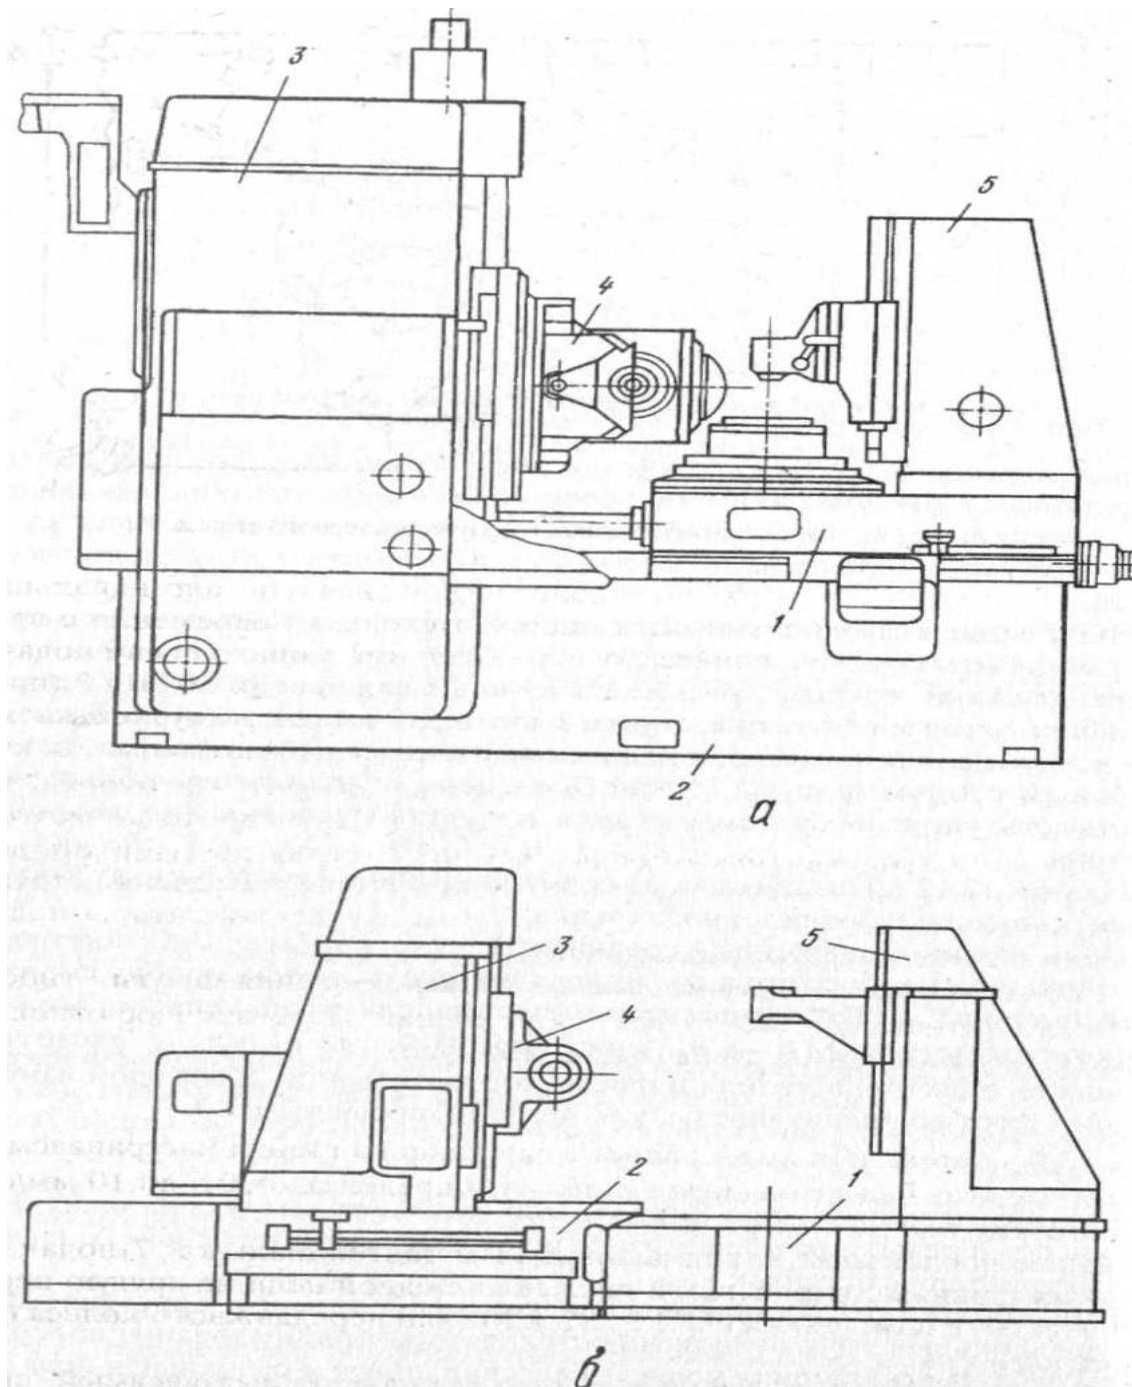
Компоновка вертикальных зубофрезерных станков с подвижным столом (а) и подвижной стойкой (б): 1 – стол, 2 – станина, 3 – стойка, 4 – фрезерный суппорт, 5 – задняя стойка.
